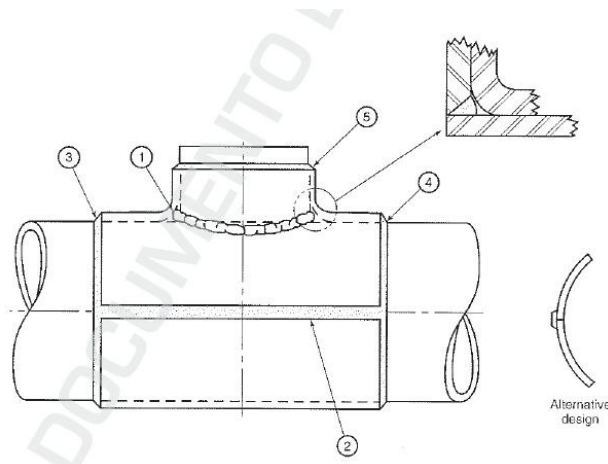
Soldadura envolvida na soldadura do acessório à tubagem [6]
